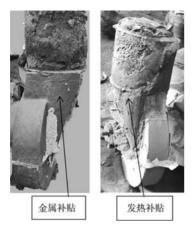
开箱后铸件法兰处的金属补贴及发热补贴 Fig. 10 Exothermic pad and metallic pad at the positions of flanges on the castings after shakeout
